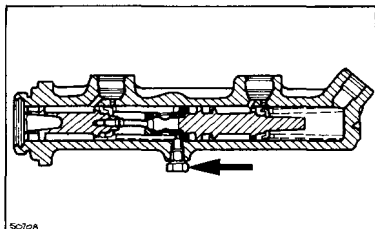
26 Стопорный винт главного тормозного цилиндра Teves
